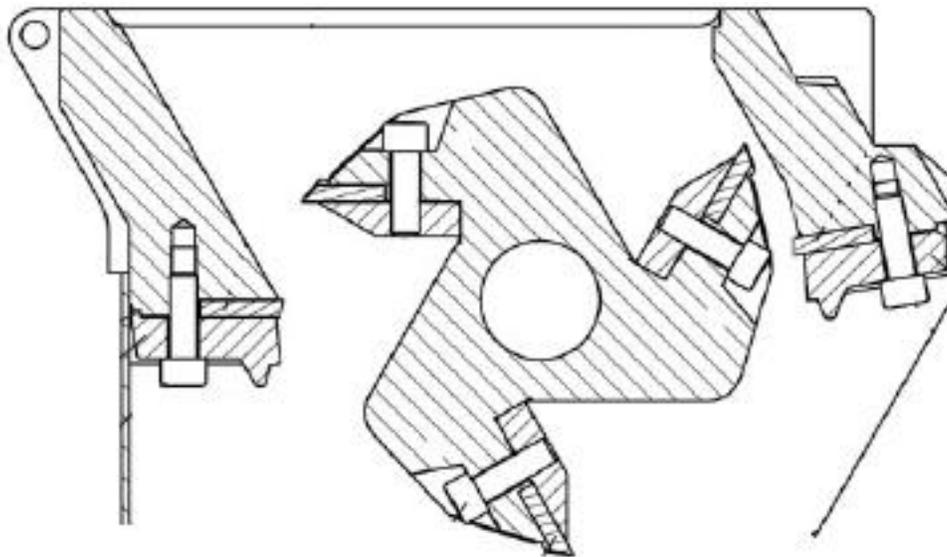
Ensamble del conjunto de cuchillas y rotor.
